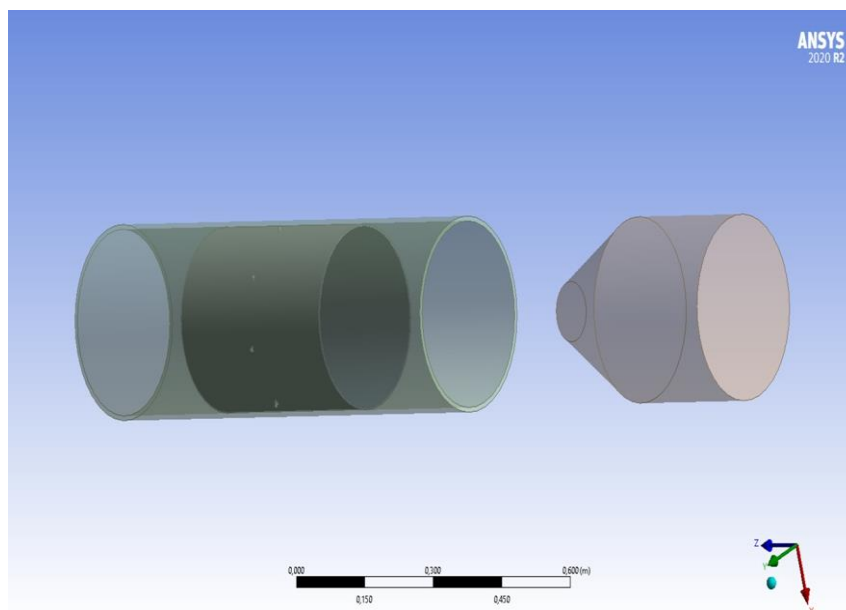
Узел сварного соединения с CPS-втулкой и очистной поршень
